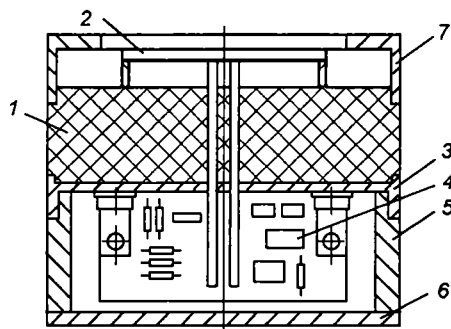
Конструкция измерительной головки РИП: 1 — корпус; 2 — ЧЭ на ЗС; 3 — основание; 4 — печатная плата ВЧ генератора; 5 — кожух; 6 — заглушка; 7 — крышка
